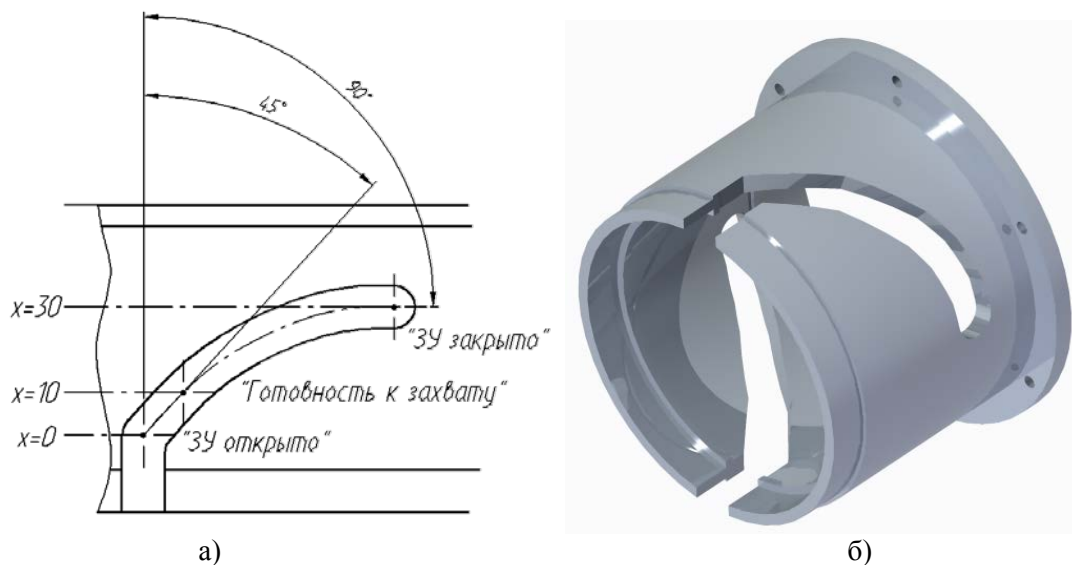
Втулка с винтовыми пазами (а) – развертка винтового паза, б) – CAD-модель втулки)
